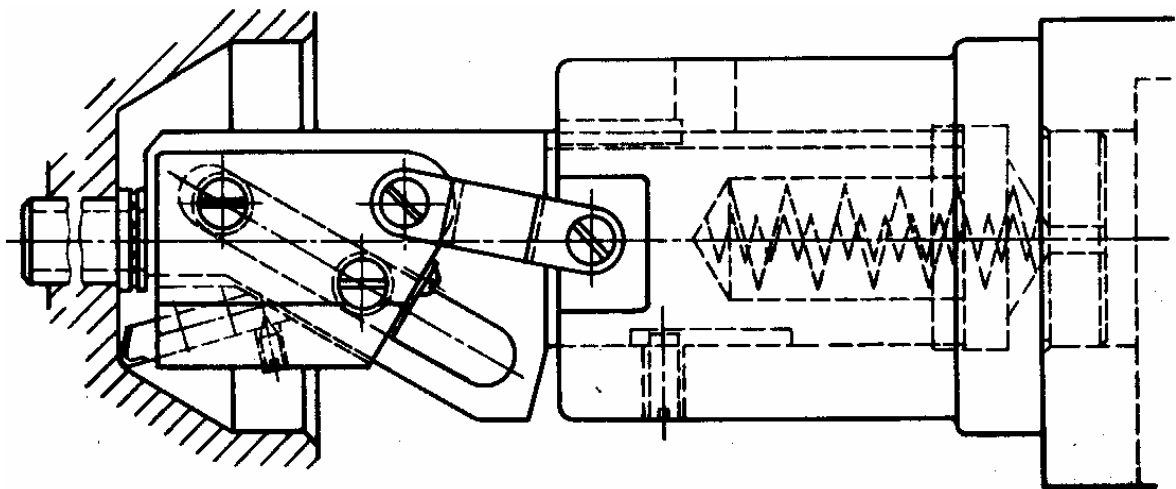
Копіювальний тримач для обробки внутрішніх конічних поверхонь
